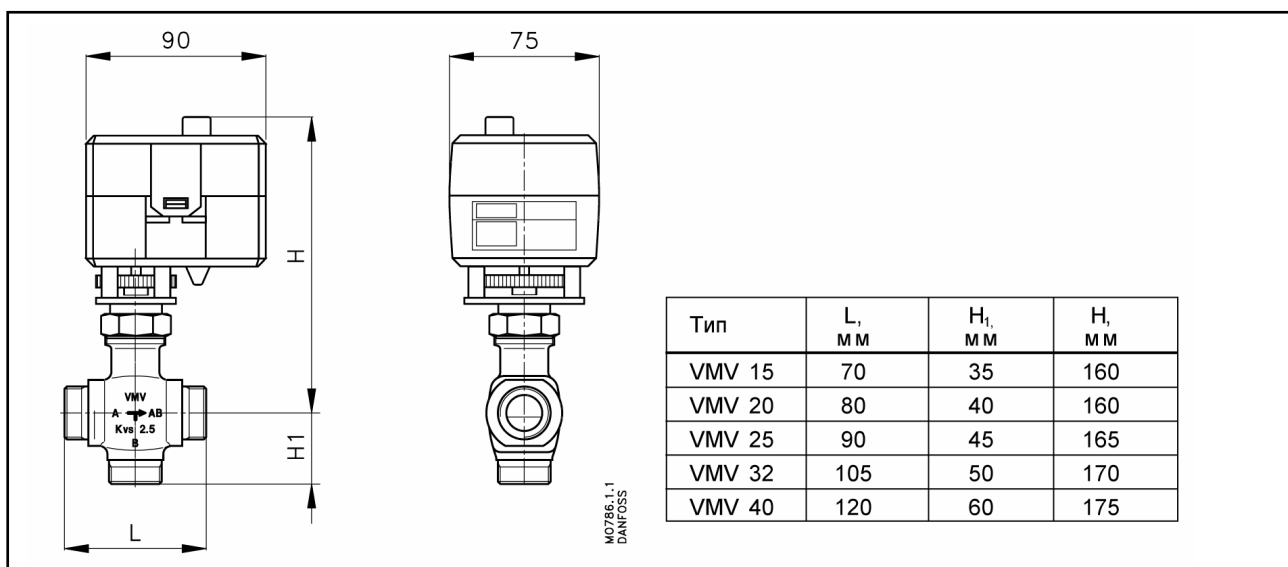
Габаритные и присоединительные размеры AMV 100 с клапаном VMV.
